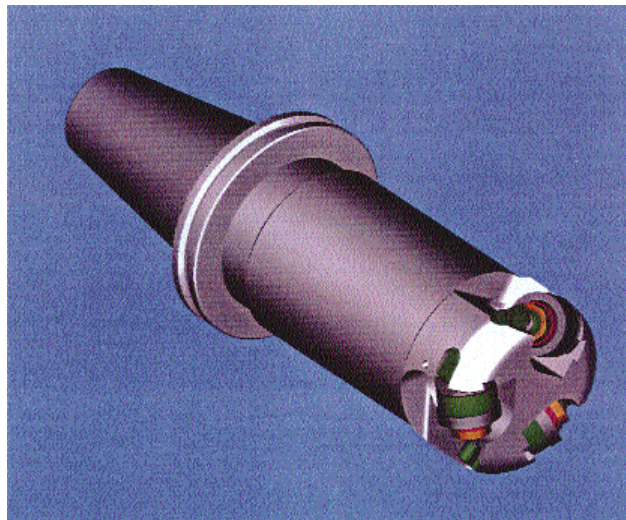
Ротаційний інструмент для чорнової обробки з трьома круглими ріжучими вставками з кераміки Si_3N_4 (фірма Rotary Technologies)
